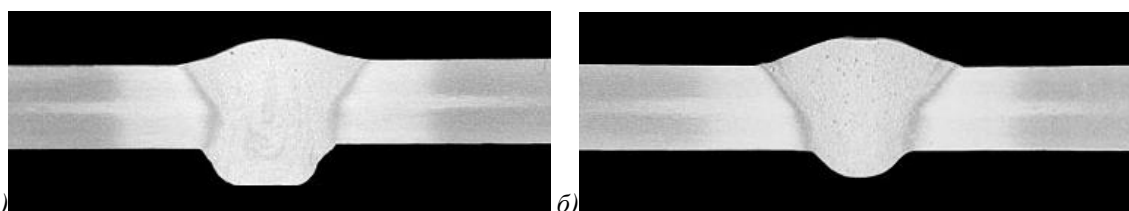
Поперечные шлифы сварных соединений листов сплава 1561 ($\delta=5,0$ мм), выполненных гибридной плазменно-дуговой сваркой:
